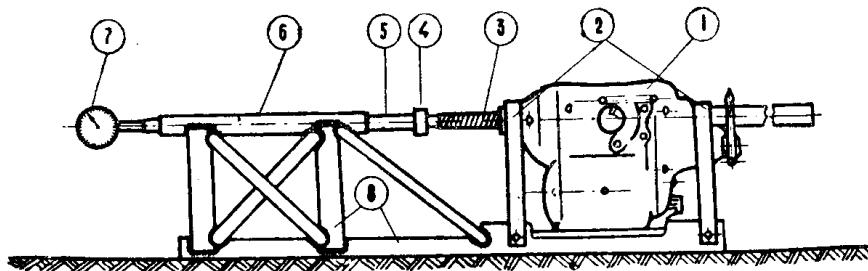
Схема установки для регулирования осевого усилия подачи шпинделя. 1—электросверло; 2—стяжные хомуты; 3—шпиндель; 4—опорный подшипник; 5—поршень со штоком; 6—цилиндр; 7—манометр
